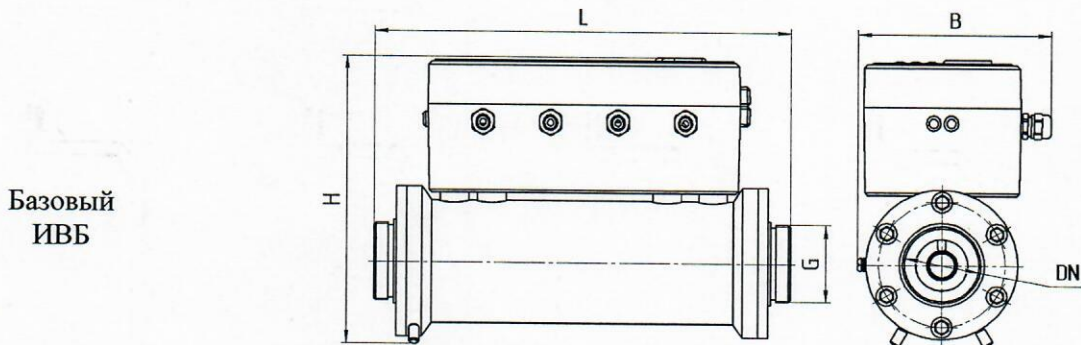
(часть 1) – Габаритные и присоединительные размеры аксиальных одноканальных комплексов, исполнения ВА, с базовым ИВБ (см. таблицу 7)
